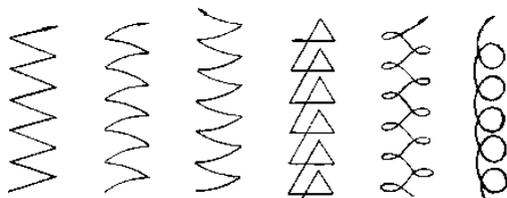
Основные траектории движения торца электрода при ручной дуговой сварке расширенных валиков
